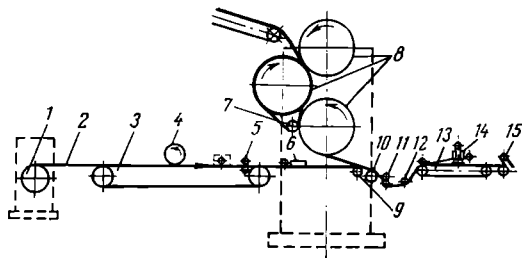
Схема агрегата АИК-300 для изоляции кромок металлокорда:
